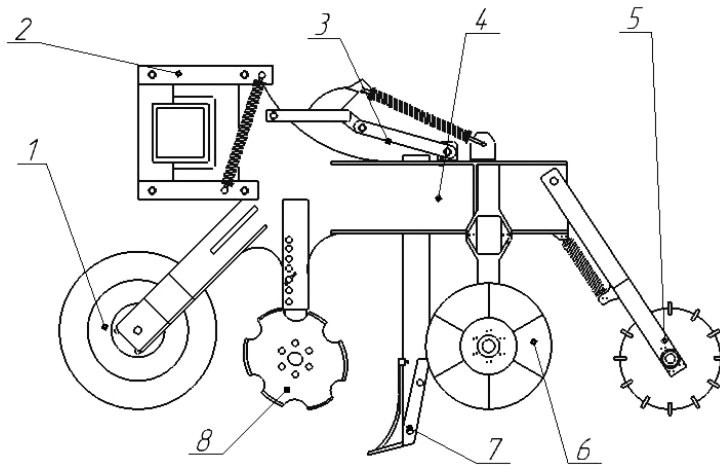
Схема секції культиватора для смугового обробітку ґрунту Stripcat: 1 – диск; 2 – паралелограмний механізм; 3 і 4 – шини передні і задні; 5 – коток; 6 – диски для формування гребеня; 7 – щілювач для внесення добрив; 8 – диск зубчатий для видалення поживних залишків.
